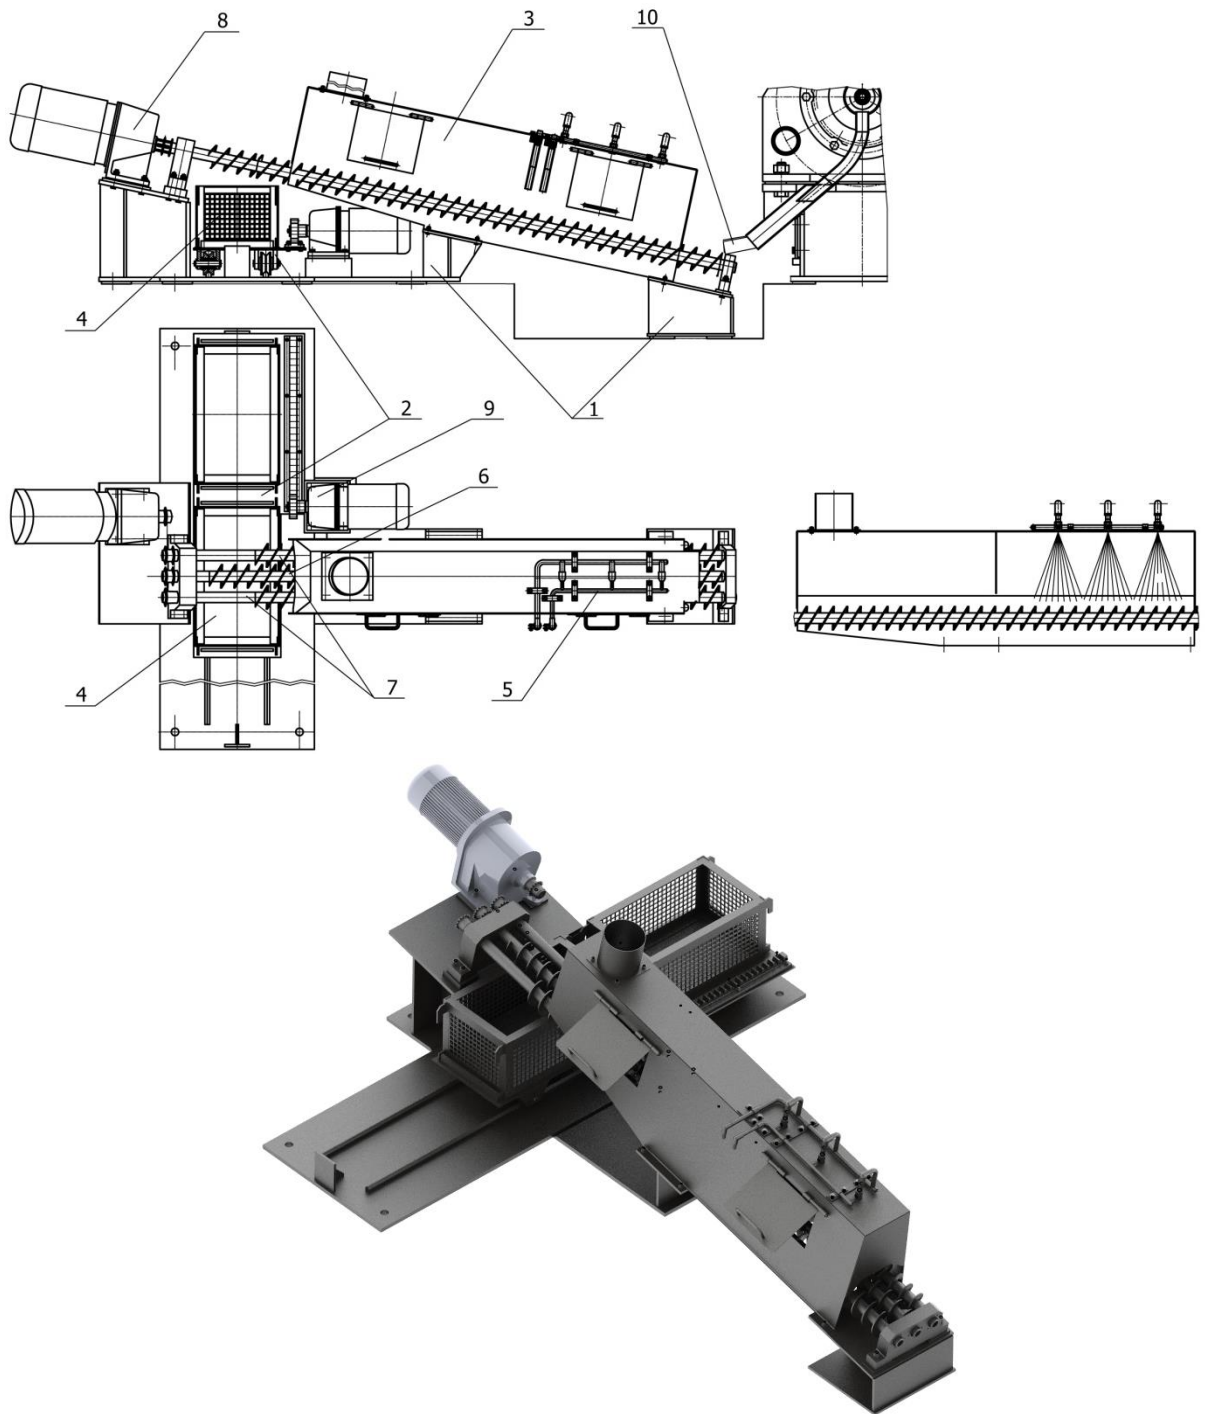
Камера контролируемого охлаждения заготовок: 1 – рама шнекового транспортера; 2 – корпус каретки; 3 – кожух; 4 – короб; 5 – устройство водовоздушного охлаждения; 6, 7 – шнеки; 8 – главный привод шнекового транспортера; 9 – привод перемещения каретки; 10 – распределитель
